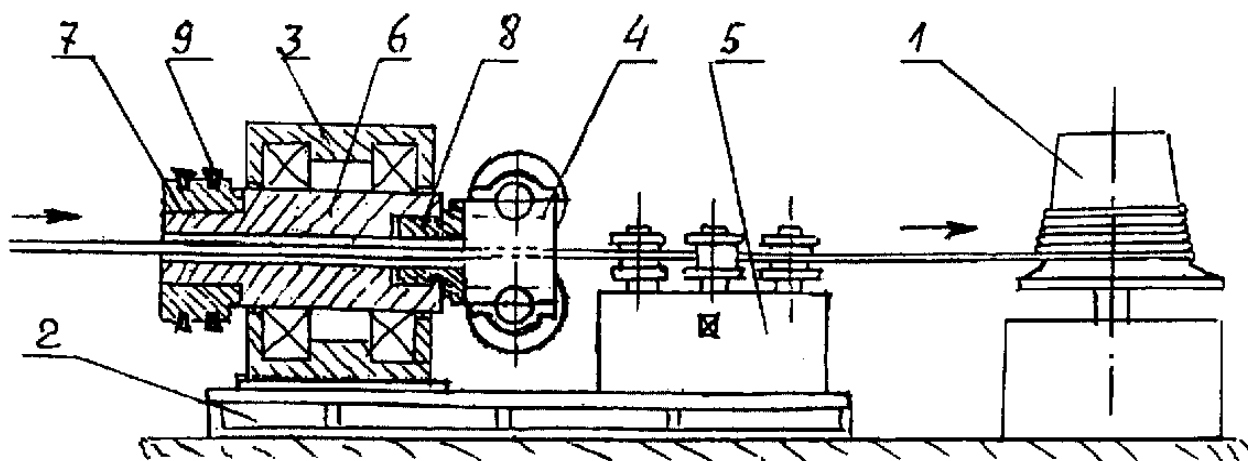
Устройство для накатки винтовой поверхности на круглой заготовке
